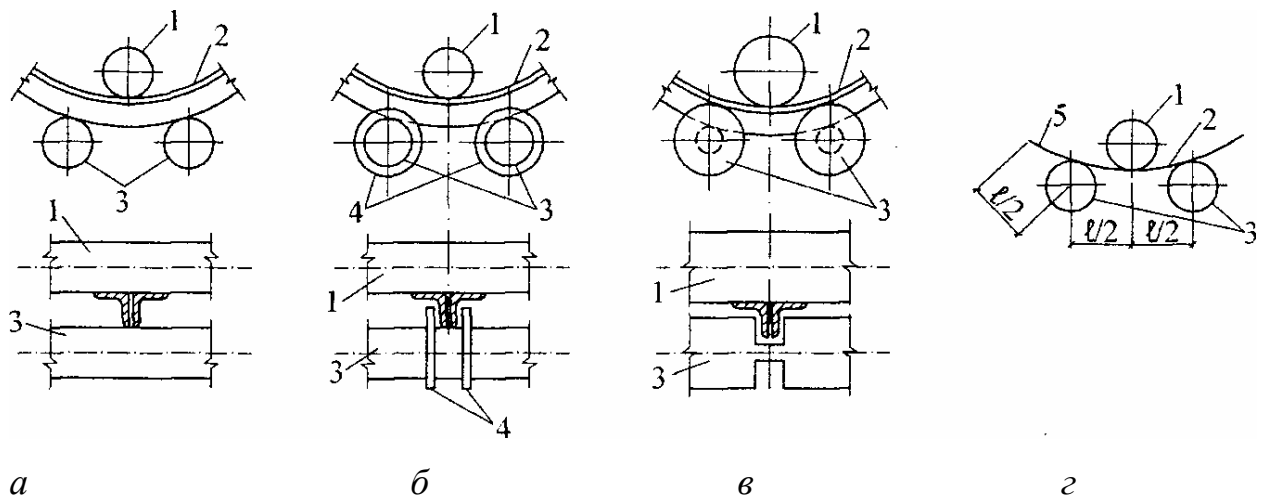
Схема гнуття на листозгинальних вальцях кутиків: *а* - з'єднання зварними прихватками; *б* - з бандажами; *в* - з прорізами; *г* - габарит прямої частини; 1 - верхній валок; 2 - завальцьована частина кутика; 3 - нижні валки; 4 - бандажі; 5 - пряма частина кутика
